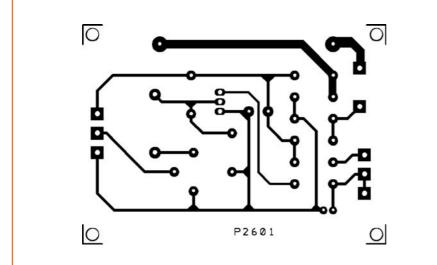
Dessin, à l'échelle 1:1, du circuit imprimé du feu à éclats ou stroboscope vu côté soudures.
